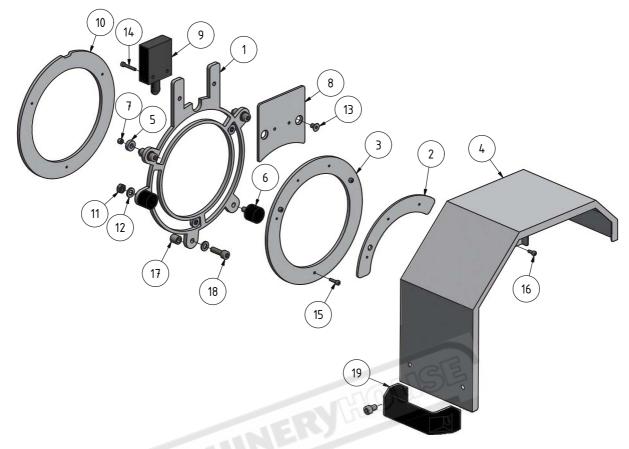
Drehfutterschutz - Lathe chuck cover
